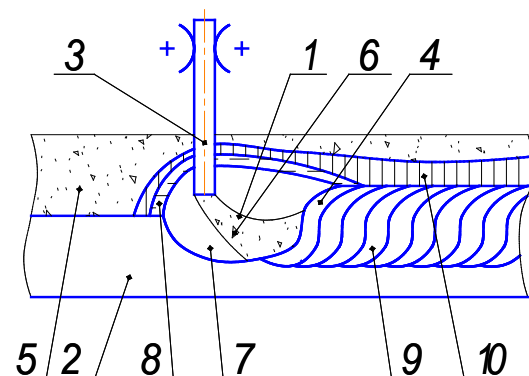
Автоматическая сварка под слоем флюса
